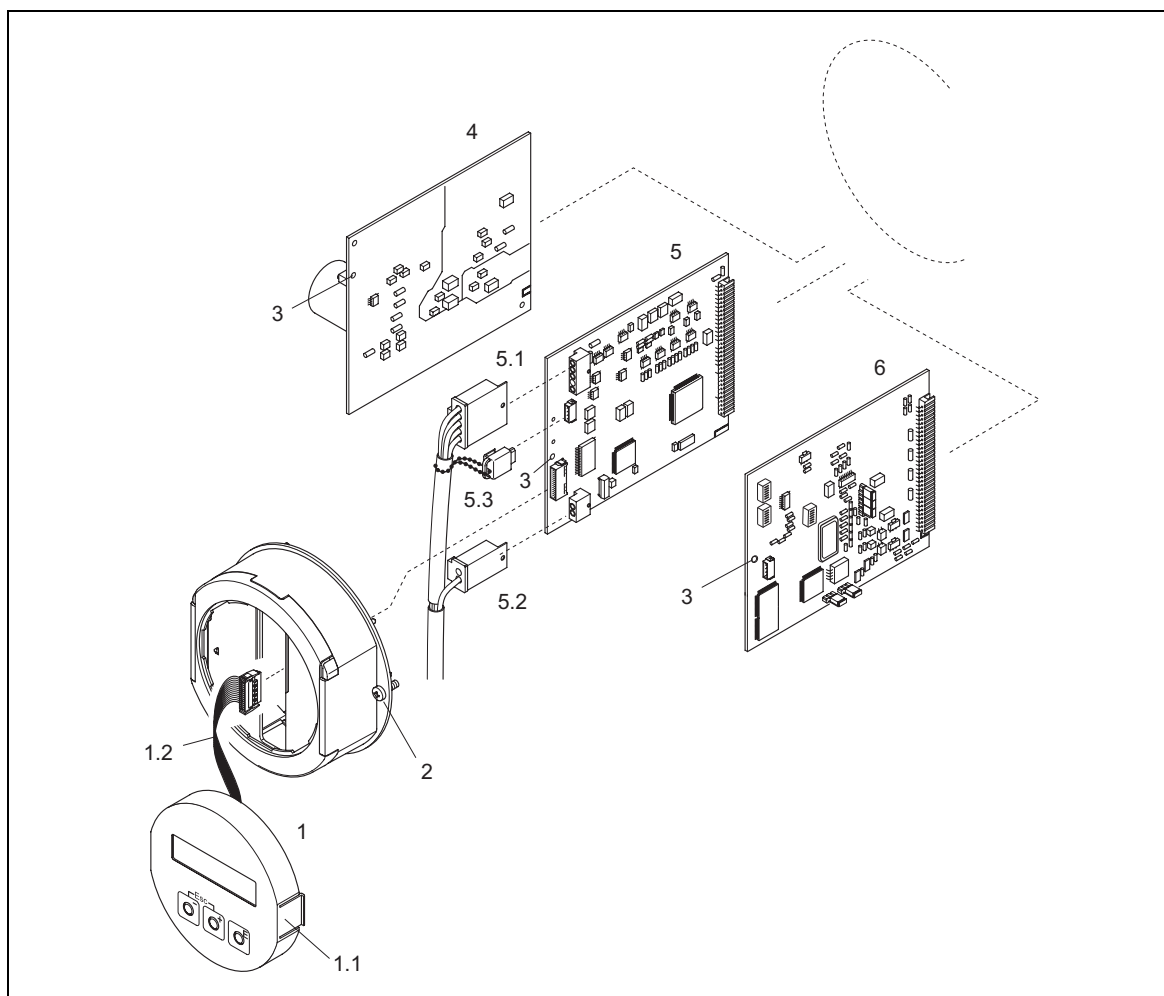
Рабочий корпус: снятие и установка электронных плат
